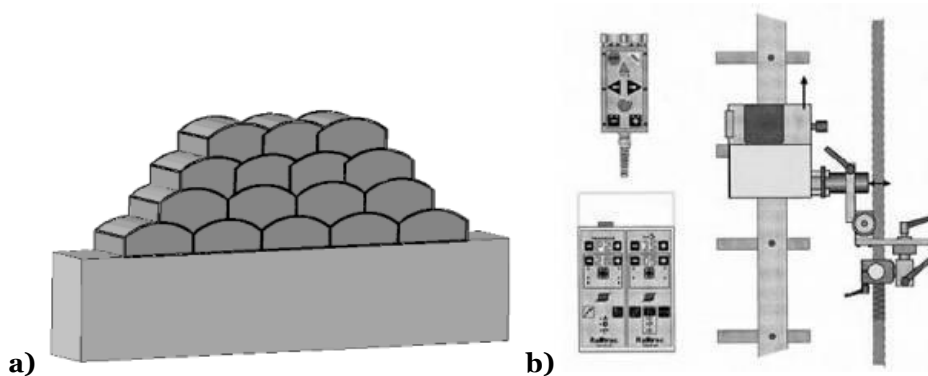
a) Secuencia de soldadura, b) Equipo Railtrac FW1000
